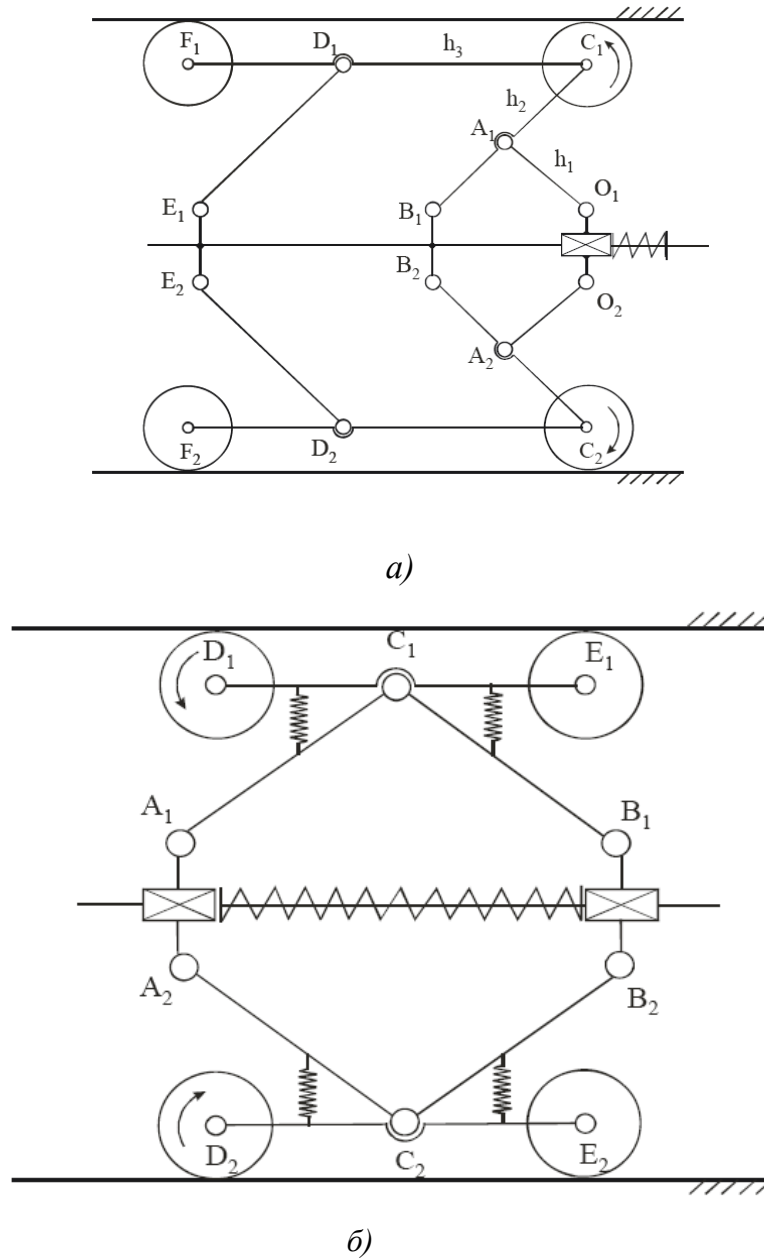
Кинематические схемы МАПКМ: а) – одноредукторный механизм; б) – двухредукторный механизм
